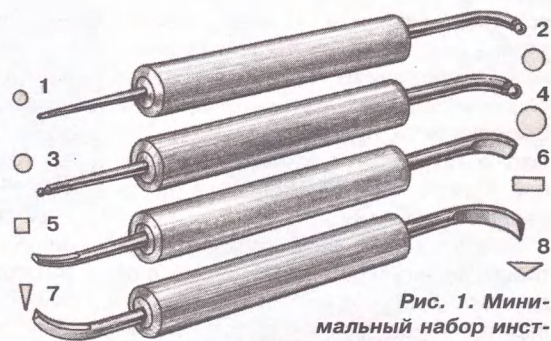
Минимальный набор инструментов для металлопластики: 1, 2, 3 — линейники (контурные стеки); 4 — выдавка шарообразная; 5 — стека давящая, узкая; 6 — стека давящая, широкая для выравнивания фона; 7, 8 — выдавки конусные.
